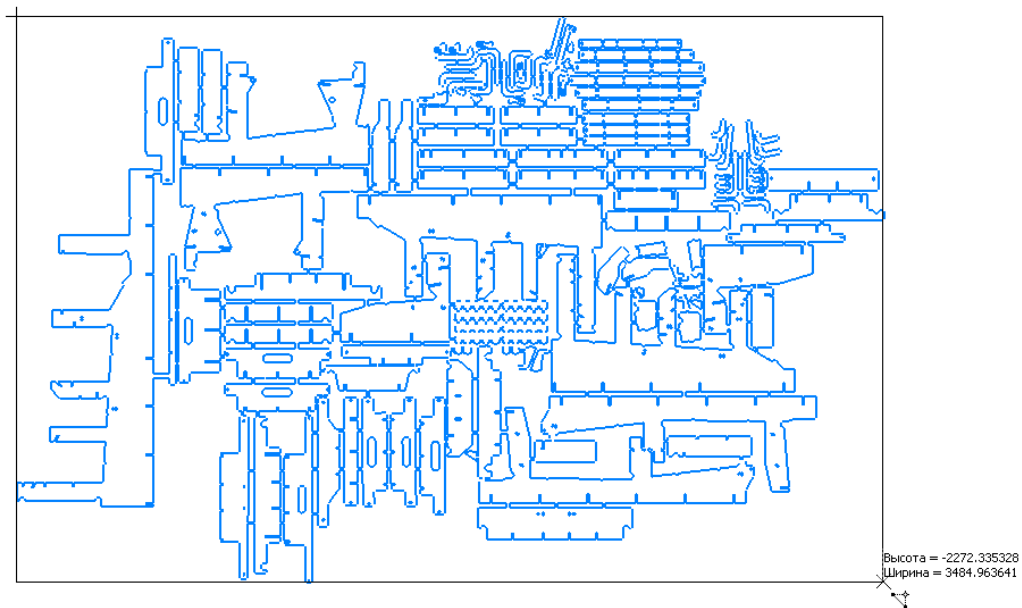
Эскиз деталей для изготовления стапеля на лазерном станке
